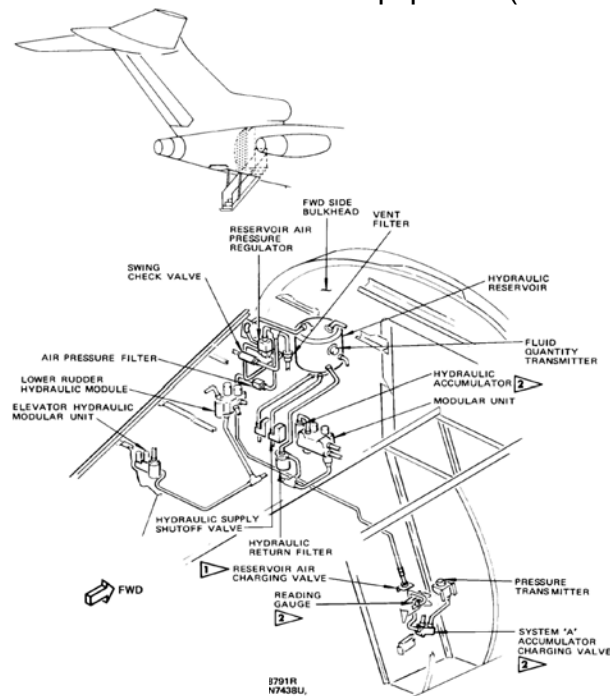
Sistema hidráulico A – Locación del equipo 3/3 (Fuente: B727-AMM)
